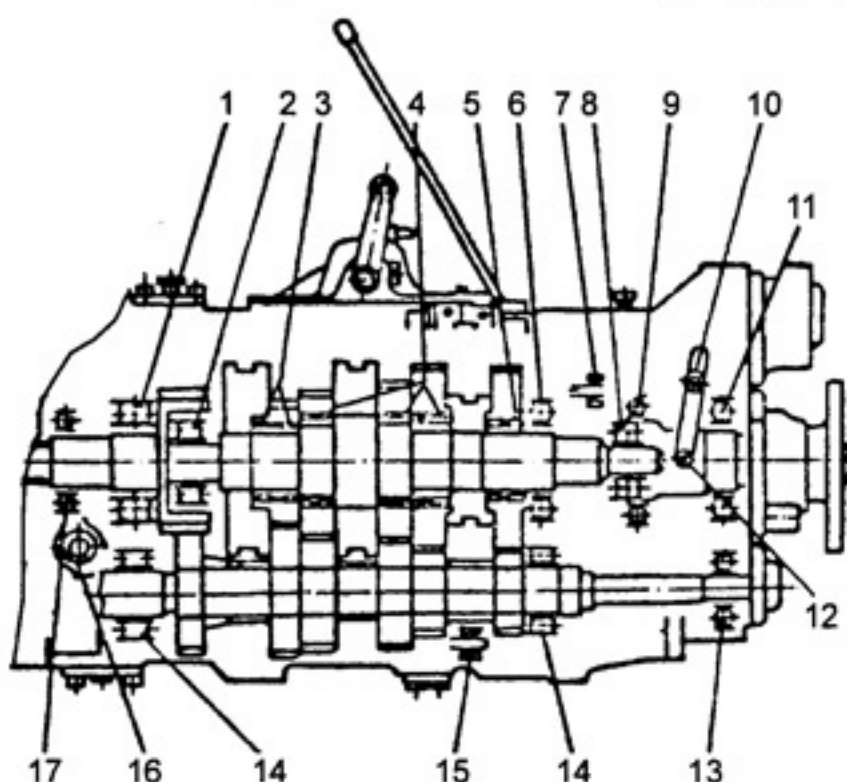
Схема расположения подшипников качения коробки передач
